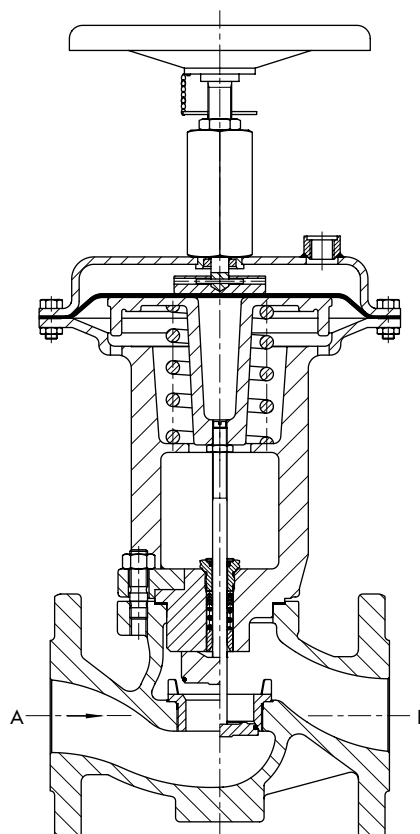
· Пневматический ОТКР-ЗАКР клапан тип 3351-1, оборудованный ручным дублером
